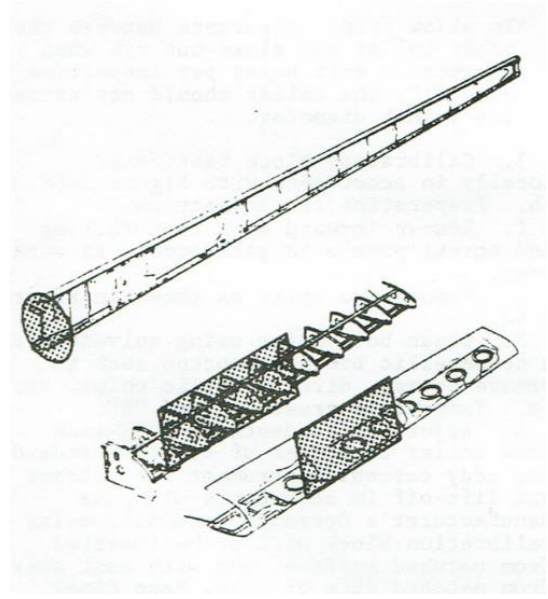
Montaje del Larguero Delantero y Borde de Ataque
